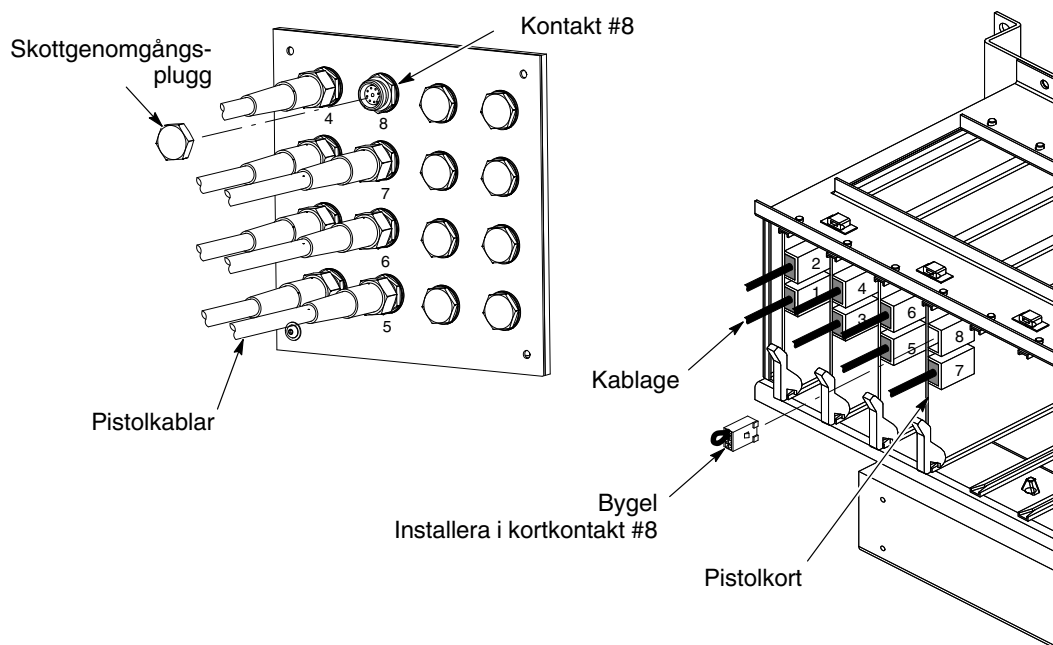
Installation av plugg och bygel - Exempel med 8 pistolers system med endast 7 pistoler
